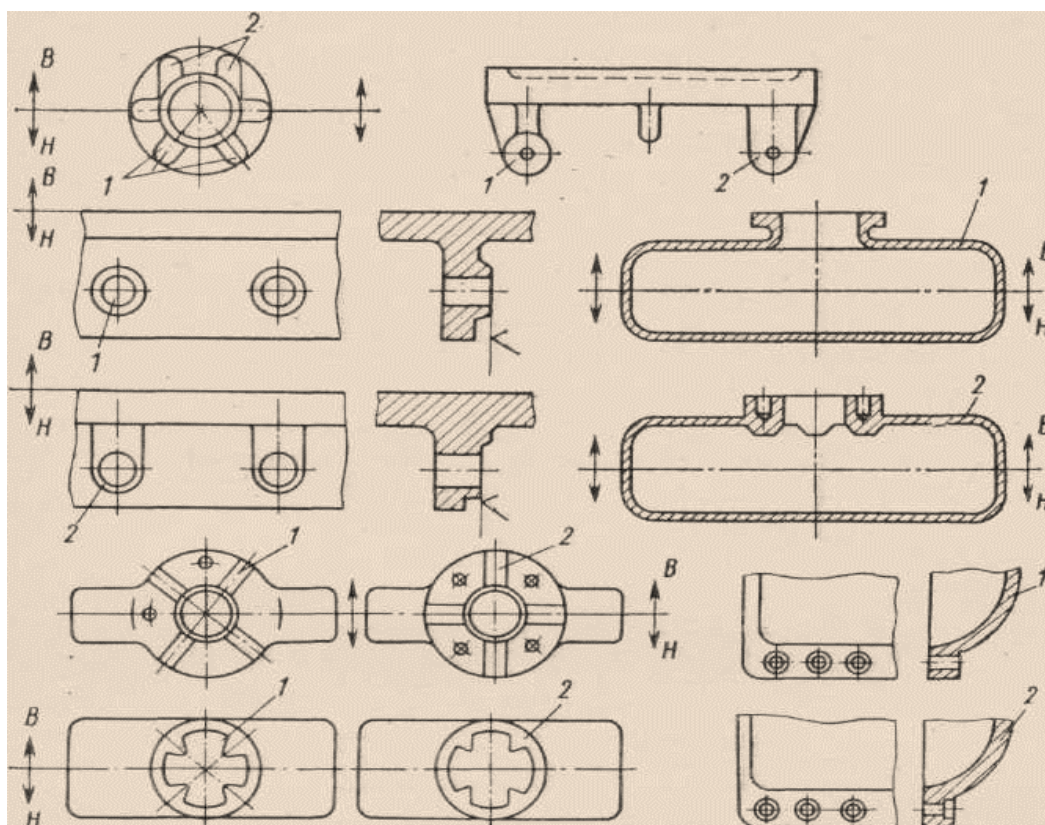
Конструкции бобышек, ребер, фланцев и отверстий в отливках;
